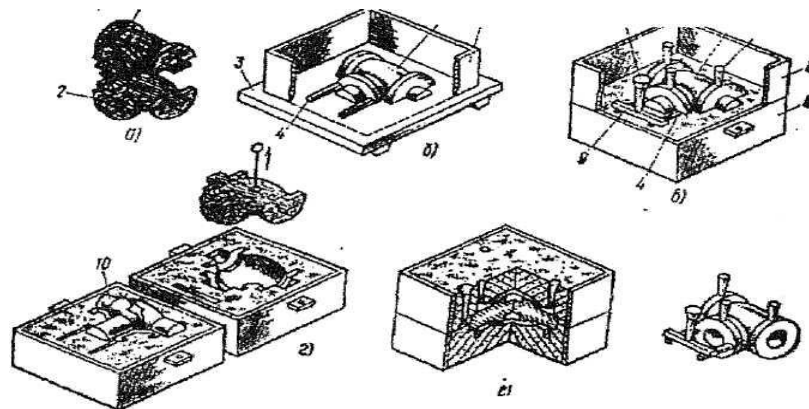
Последовательность операций изготовления литейной формы корпуса вентиля
